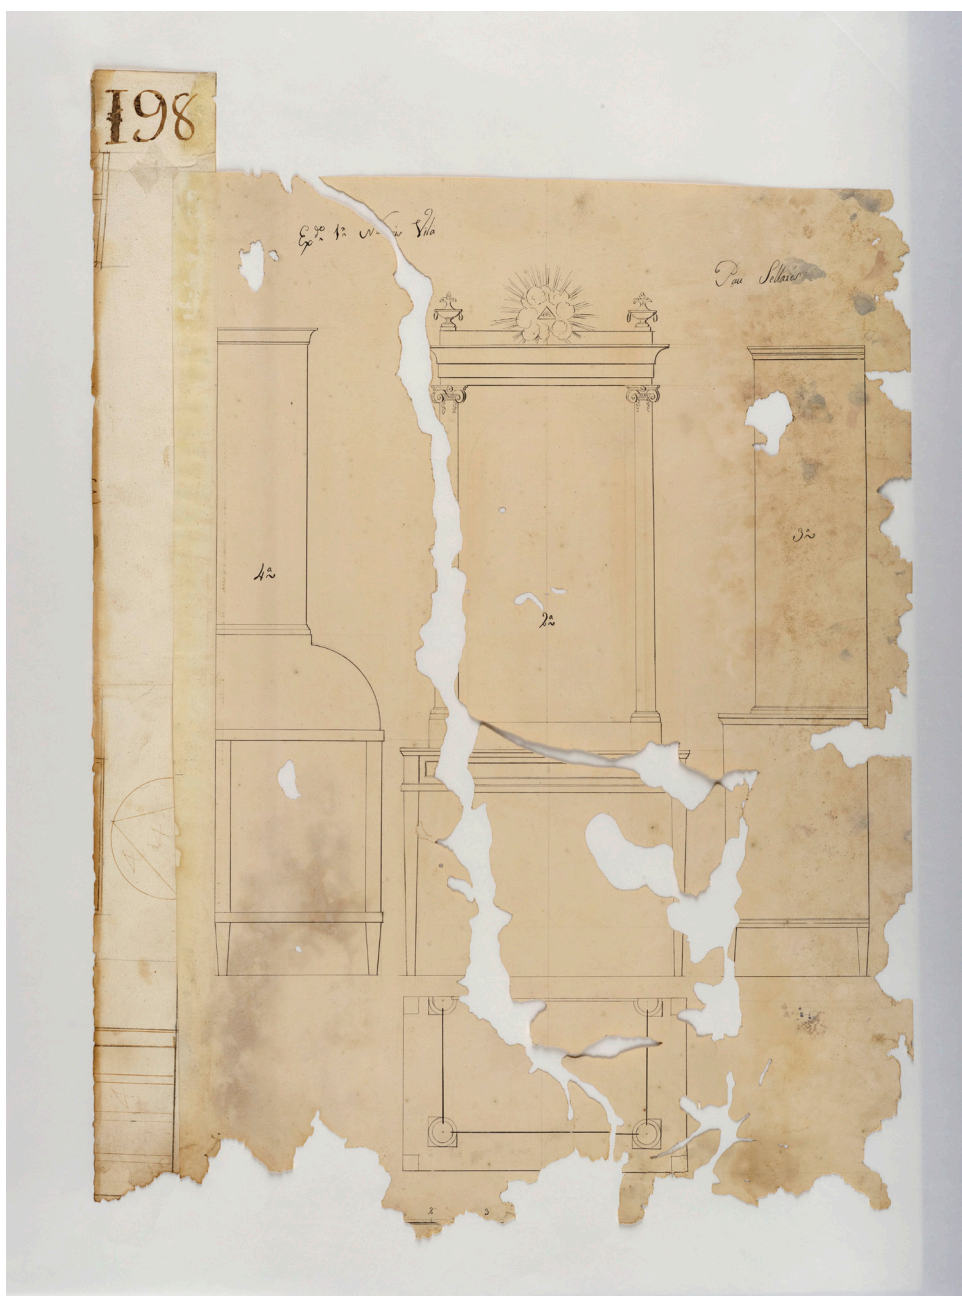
P. 198. Pau Sellarés. Mesa con escaparate, planta y alzado. Escritorio de tambor con librería de perfil. Cómoda librería de perfil
